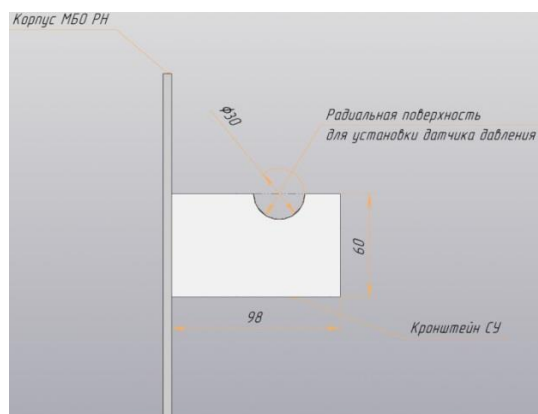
Расчетная схема конструкции кронштейна СУ
